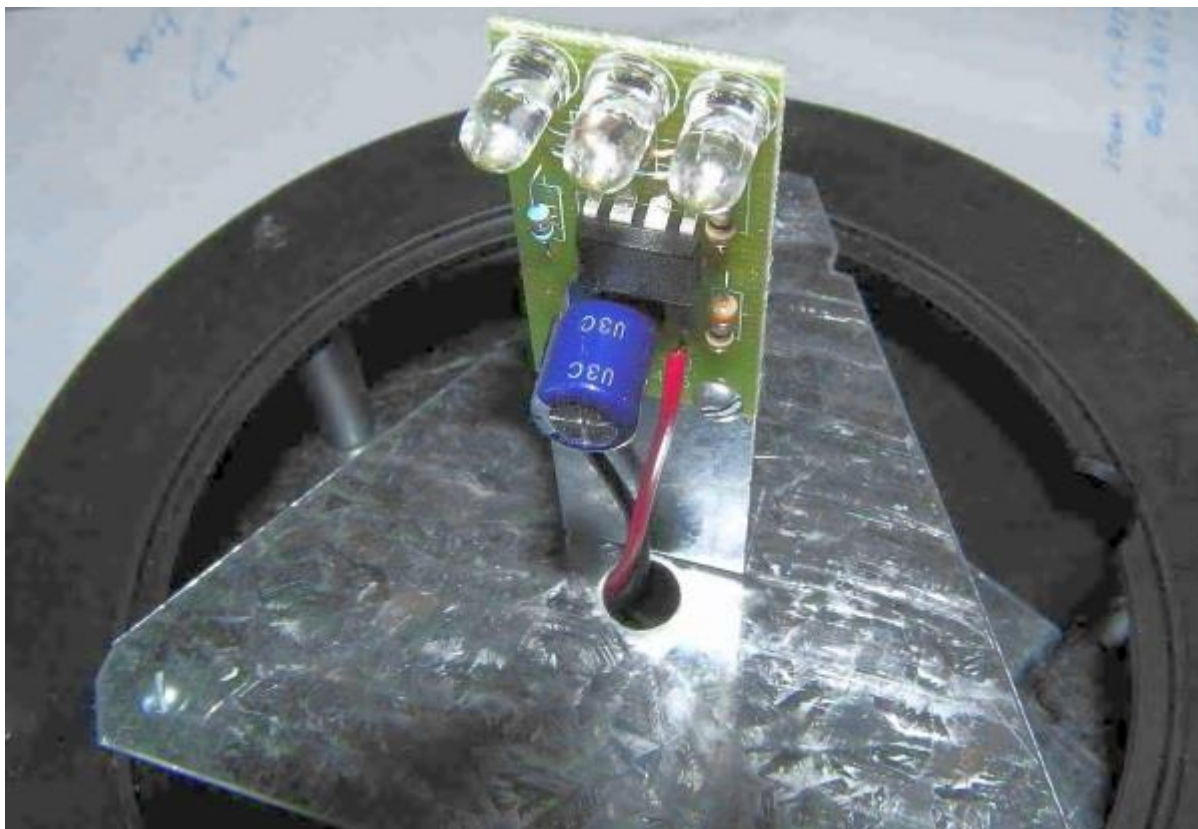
Вид на печатную плату, устанавливаемую в корпусе
